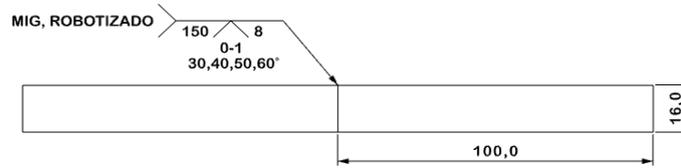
Diseño de unión para el soldeo de placa AISI 1018 con GMAW robotizado.
